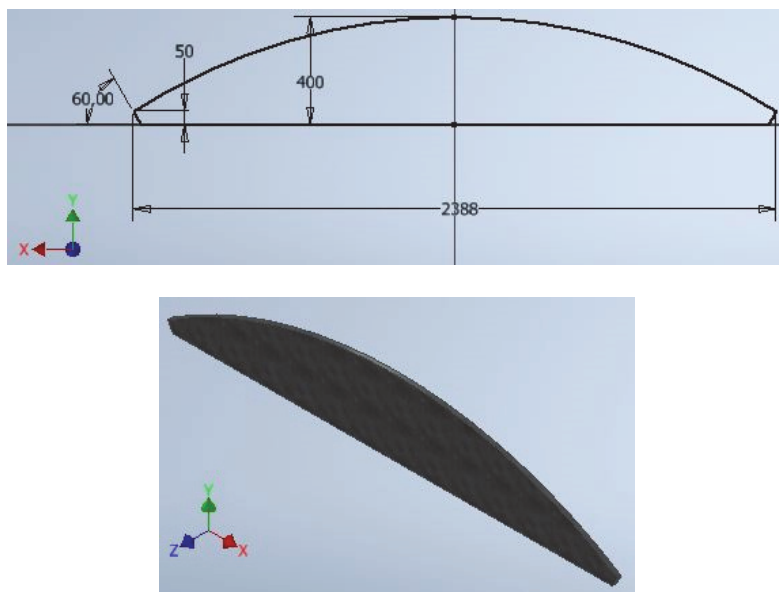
Центральный стрингер (эскиз и готовая деталь)
